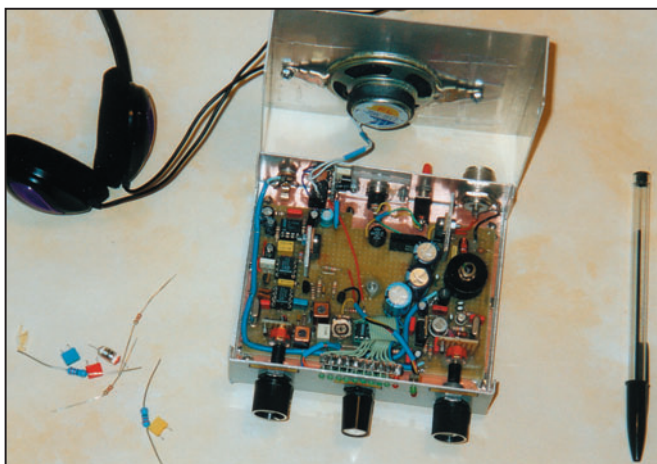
Le boîtier ouvert laisse voir le montage terminé.
